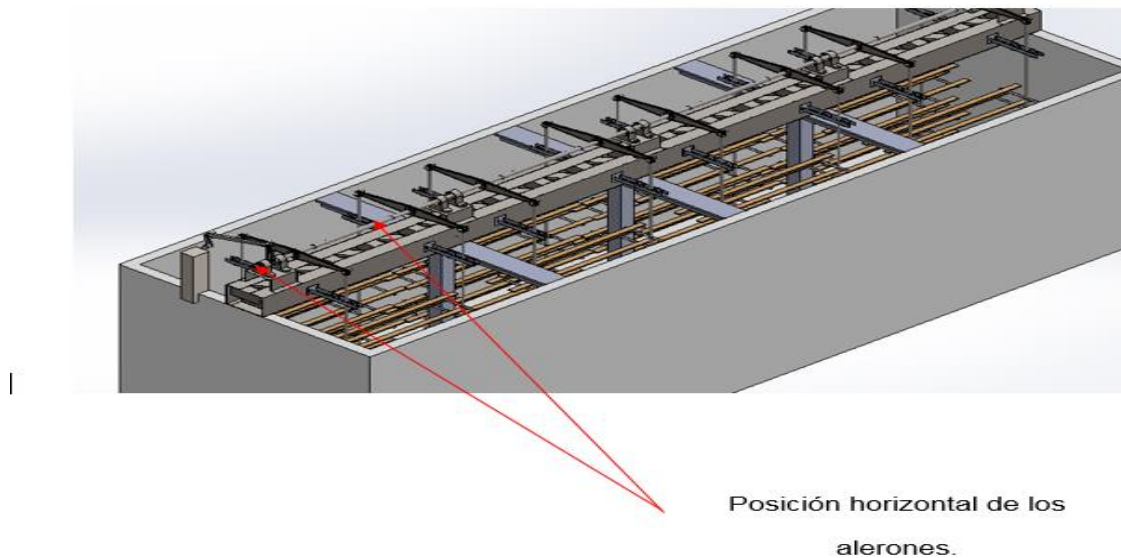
Ensamblaje del alerón con los elementos agitadores.
